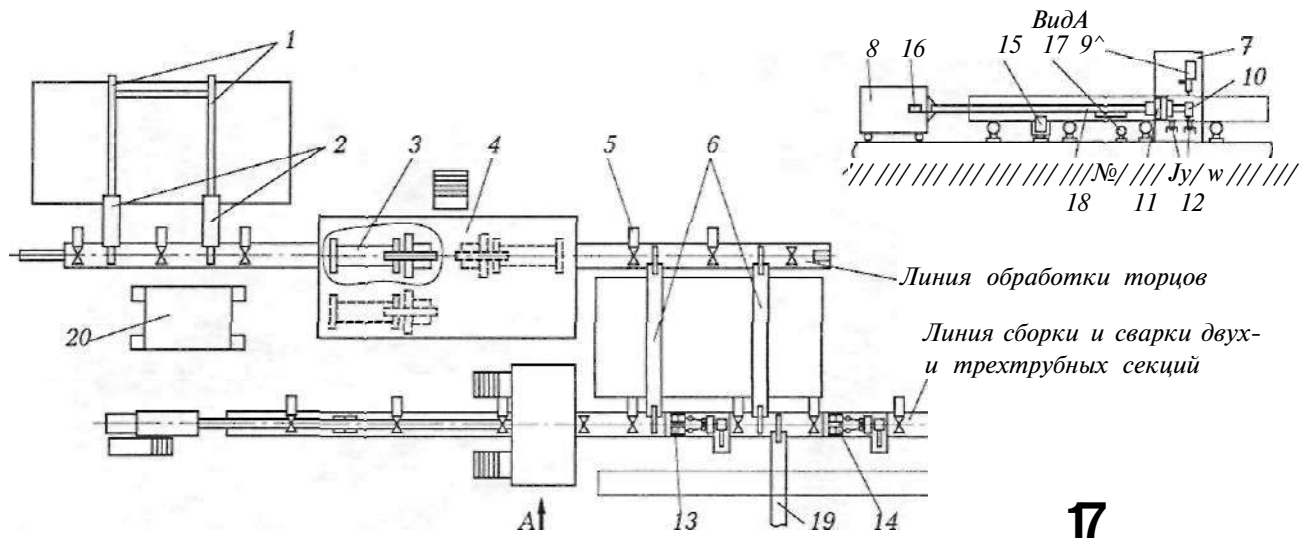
Схема трубосварочной базы БТС-142В:
